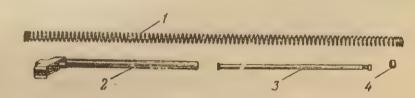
Возвратный механизм: Возвратная пружина; 2 — направляющий стержень; 3 — подвижный стержень; 4 - муфта
